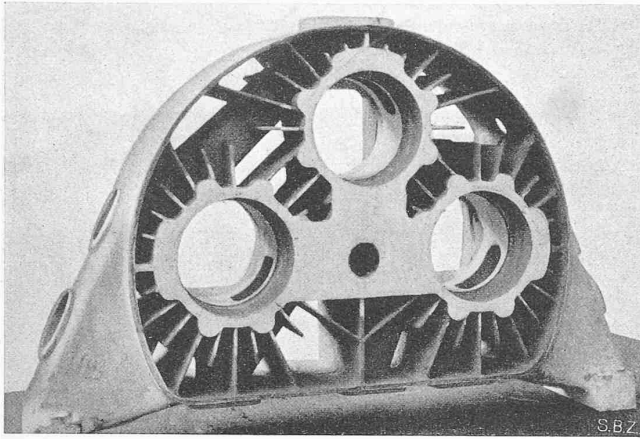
Siluminguss-Gehäuse eines dreizylindrigen luftgekühlten Rotations-Kompressors
